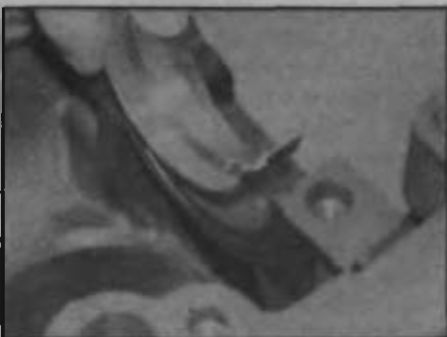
Установка вкладыша коренного подшипника в блок цилиндров
